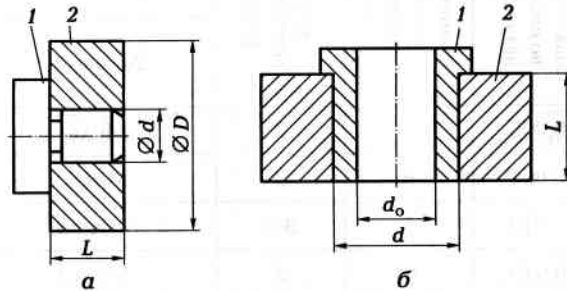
Сборочный чертеж прессового соединения деталей 1 и 2:
